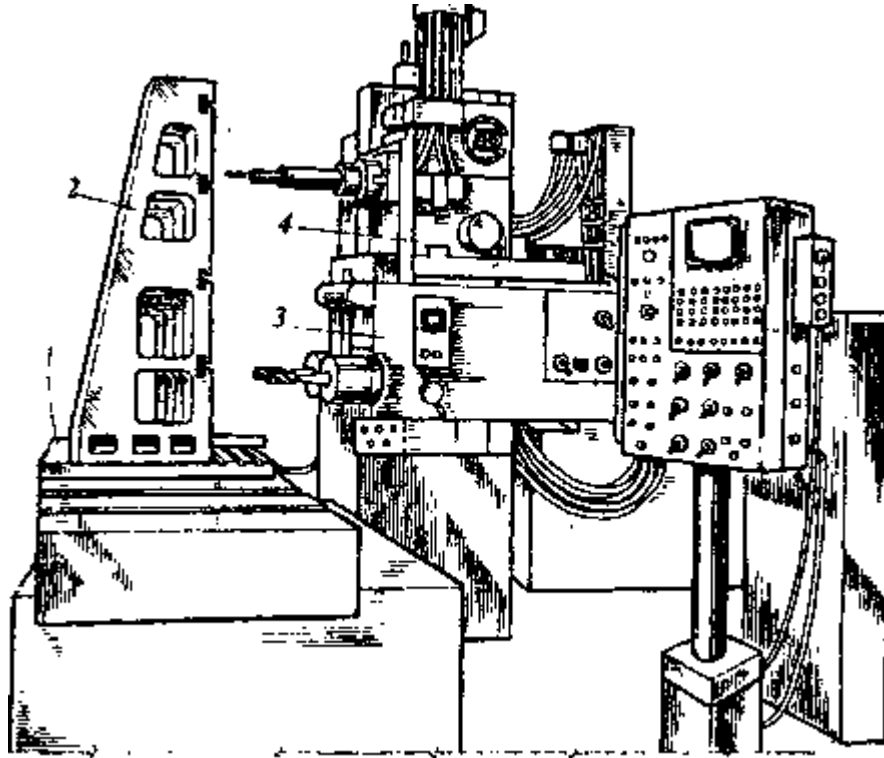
Копіювально-фрезерний верстат з числовим програмним керуванням
